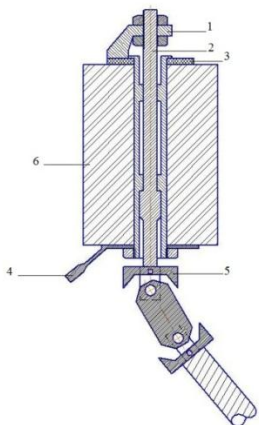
Схематическое изображение технологической приставки: 1 - твердосплавный резец; 2- стальной стержень; 3- образец; 4- высоковольтный коннектор; 5- двойной (спаренный) кардан; 6- керамический изолятор
